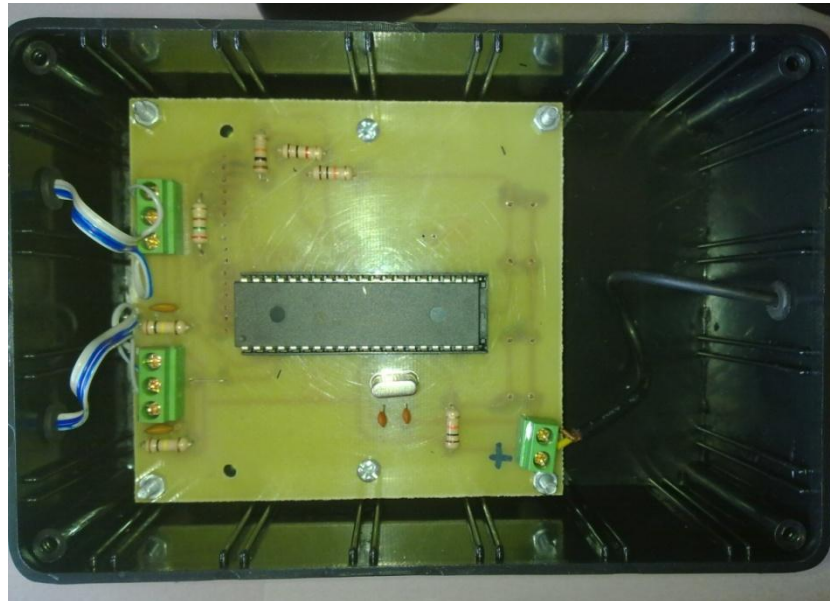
PLACA MONTADA EN EL CHASIS.
